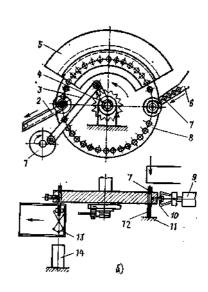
Автоматическая линия для горячей штамповки стержневых изделий:
